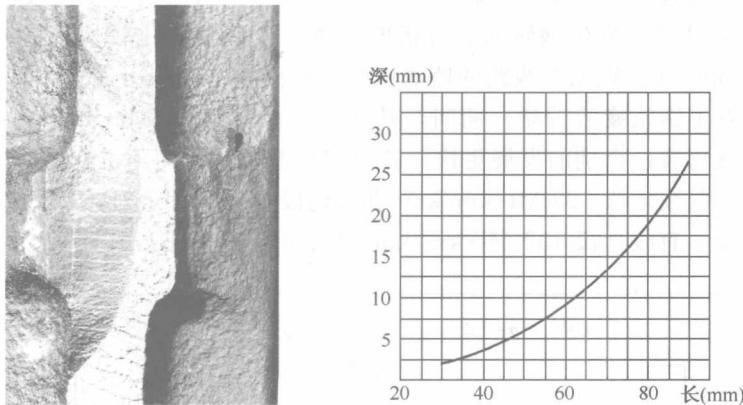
钢轨气压焊接头下腭轨腰水平裂纹及其扩展曲线
